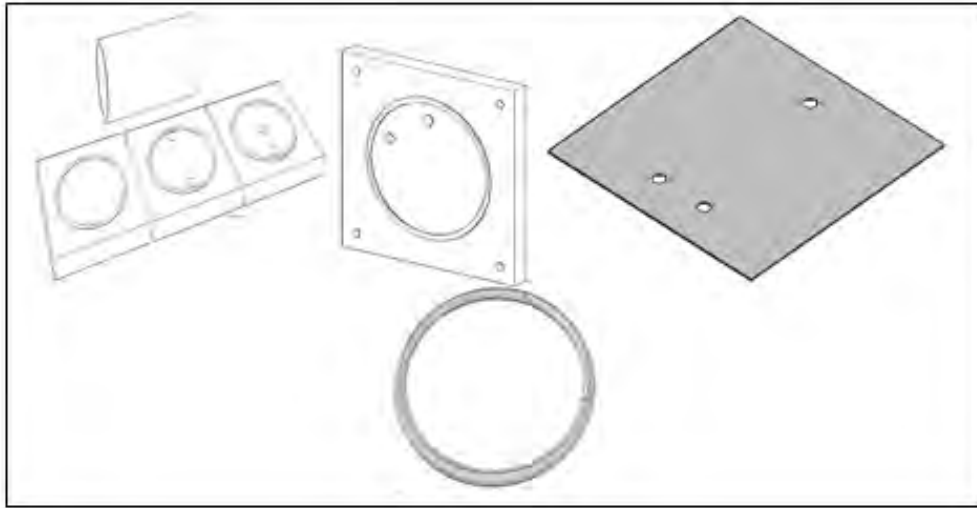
Diseño de piezas y/o componentes que se utilizan en el ensamblaje de la celda.
